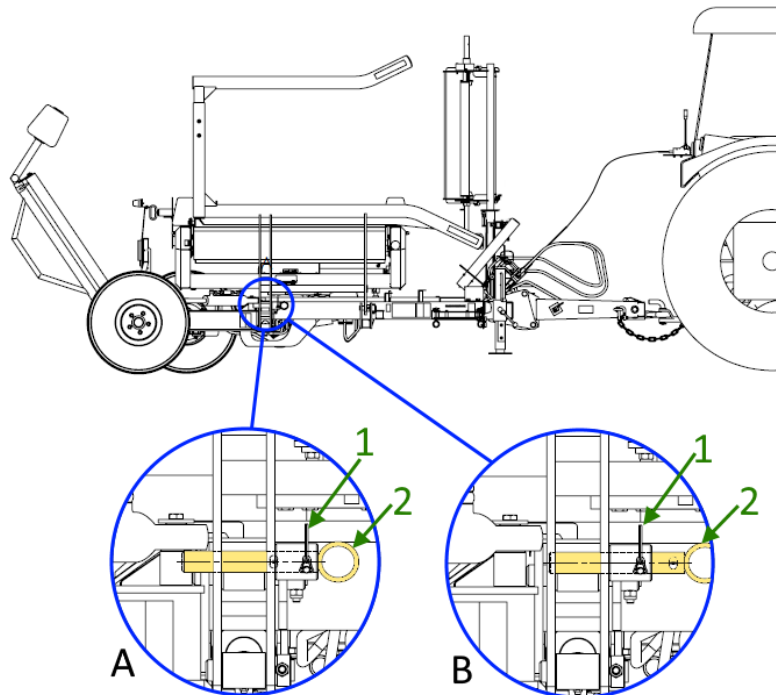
Verrouillage de la position du bras de chargement : A – position de transport, B – position de travail, 1 – goupille d'arrêt du goujon de verrouillage, 2 – goujon de verrouillage
